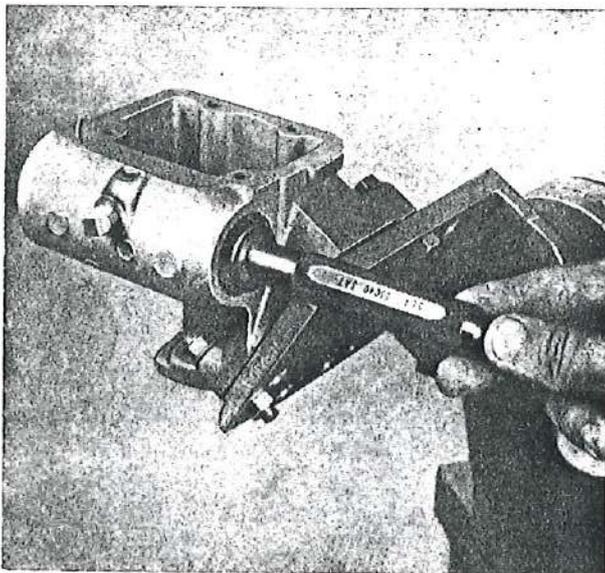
Desmontaje del anillo exterior del rodamiento superior del tornillo sin fin, mediante el útil A. 66040.
